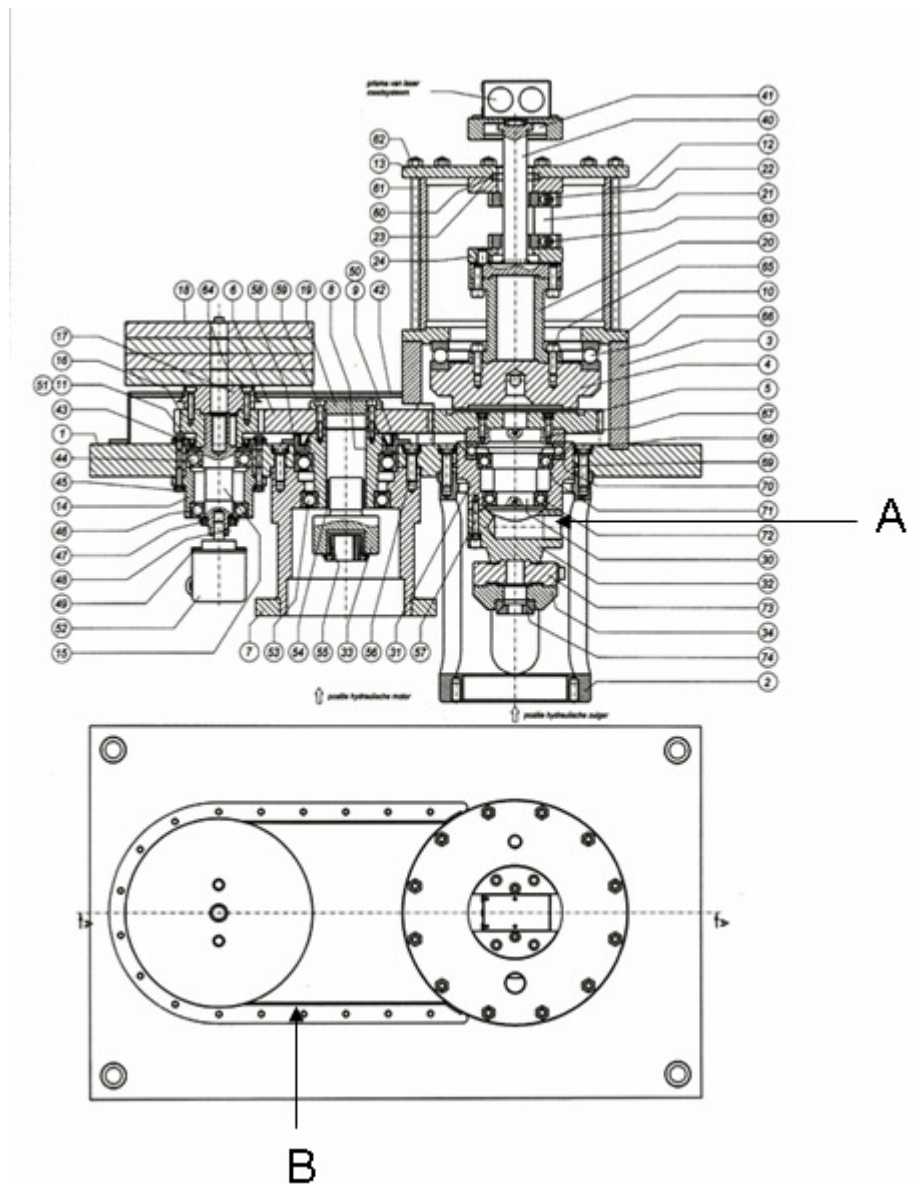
Plan van de opstelling met A de afvoer door de lagers en B het gat in de omkasting
